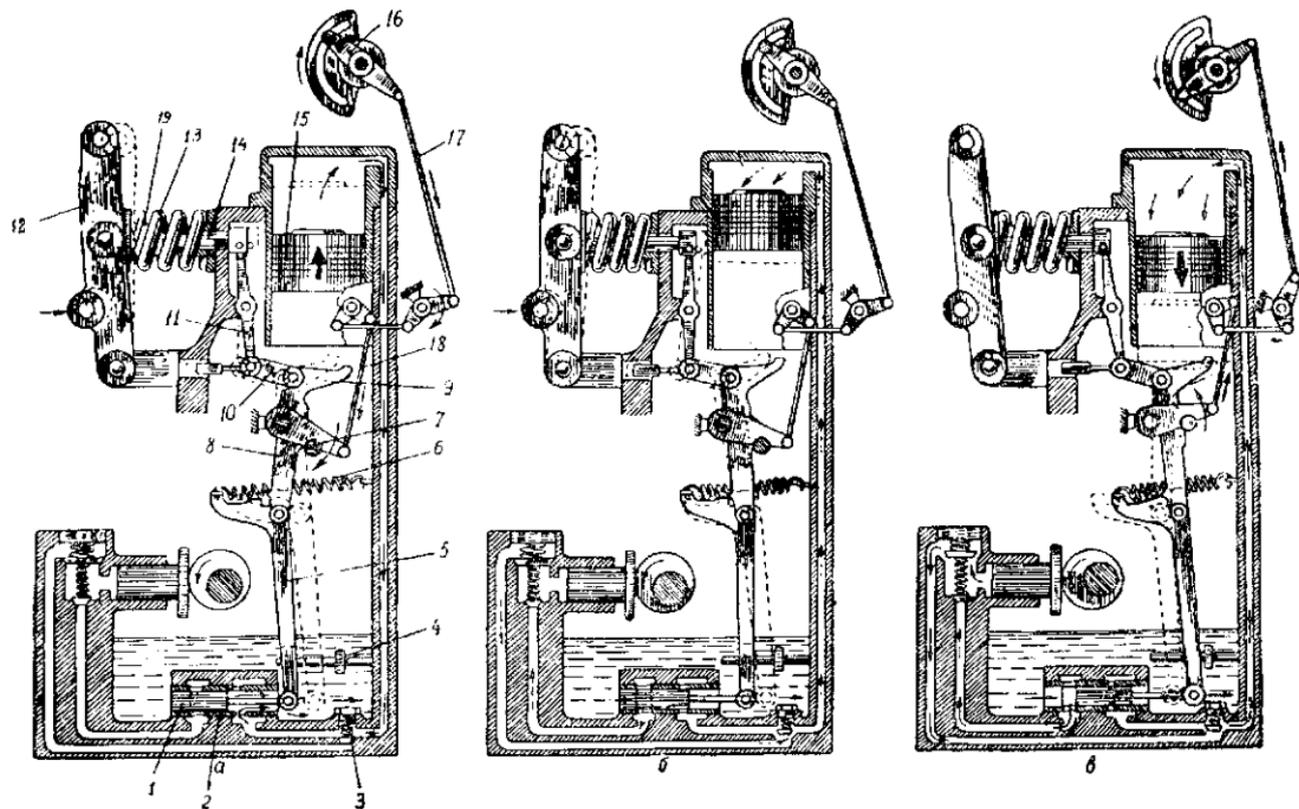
Схема ручного и автоматического управления работой навесной системы трактора «Беларусь»: 1 — золотник; 2 — гильза; 3 — обратный клапан; 4 — упорное кольцо; 5 — нижнее звено внутреннего рычага; 6 — пружина; 7 — кривошипный вал; 8 — верхнее звено внутреннего рычага; 9 — отводка верхнего звена; 10 — направляющая вилка; 11 — промежуточный рычаг; 12 — серга силового регулятора; 13 — пружина силового регулятора; 14 — шток; 15 — рабочий цилиндр; 16 — рукоятка; 17 — 18 — тяги; 19 — гайка силового регулятора. а — опускание орудия; б — установка на заданную глубину обработки или высоту подъема; в — автоматическое включение подъема.
